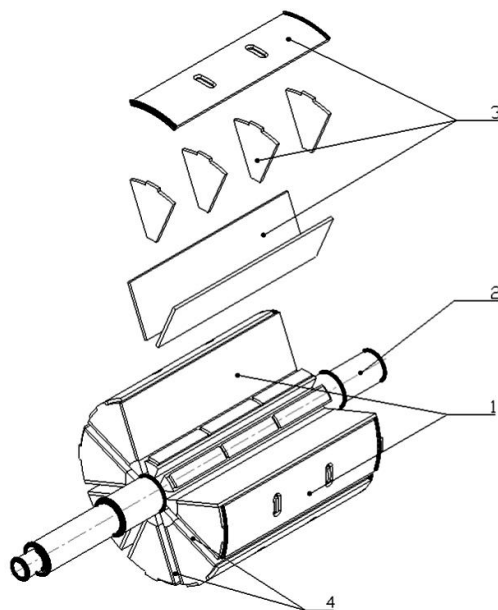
Ротор парового ротационного двигателя: 1) Ротор двигателя в сборе; 2) Вал ротора; 3) сборная часть барабана; 4) Пазы для установки щеток
